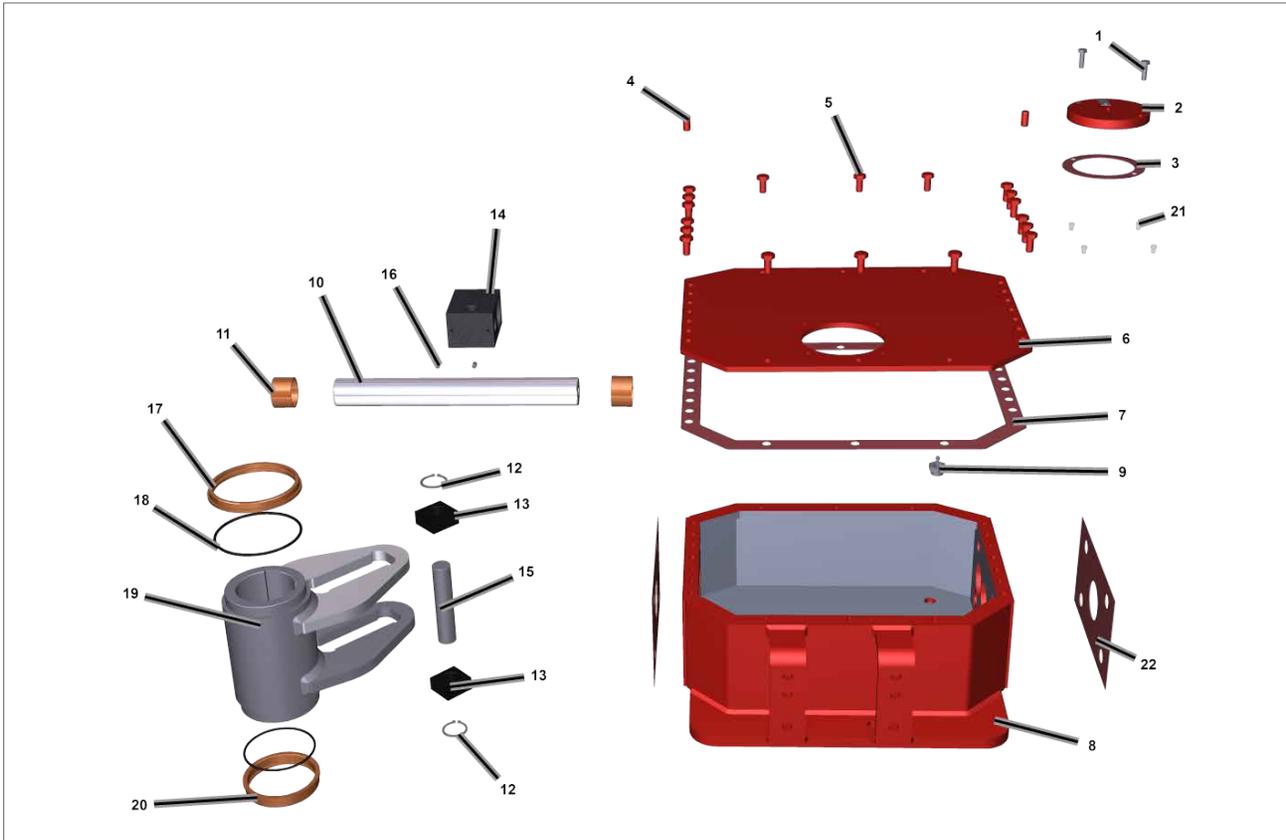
Corpo central (soldado) (atuador de tamanho 065, 85, 100, 130, 161, 350)
